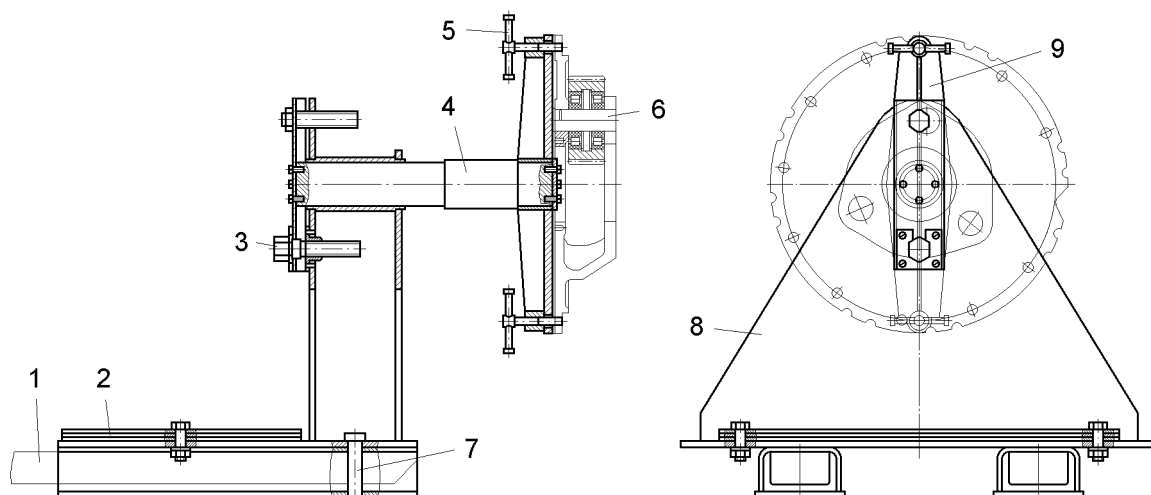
Приспособление для снятия и установки водила с сателлитами:
